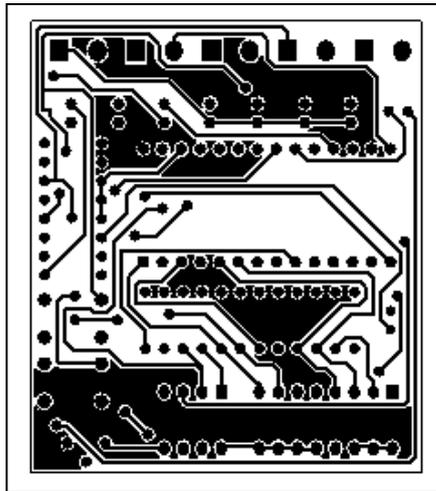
Cara superior del PCB de la Tarjeta Universal del ISD.
